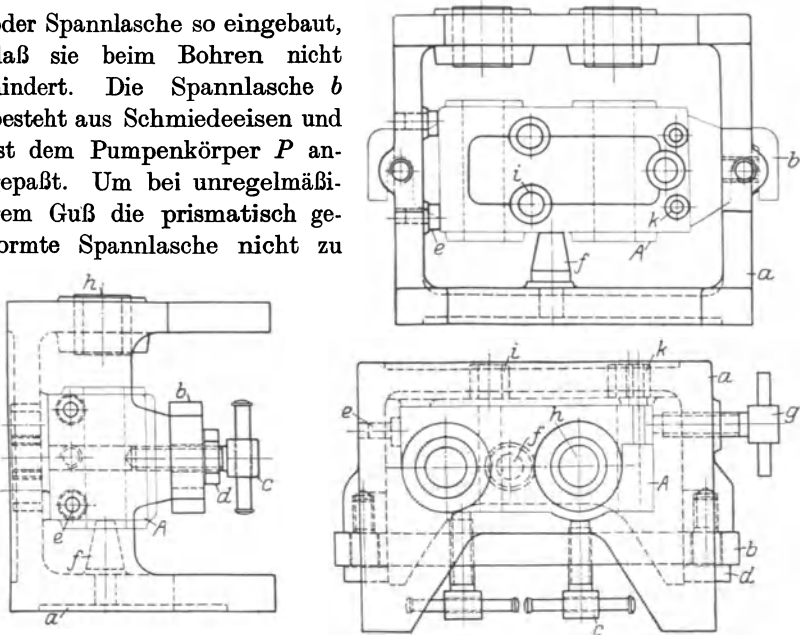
Bohrvorrichtung für Leit- und Zugs spindleager.
